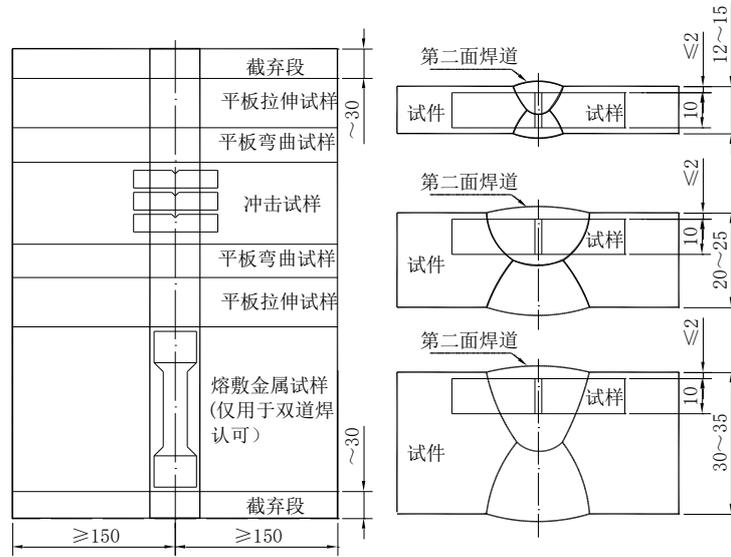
埋弧双面单道焊工艺试件的取样位置
